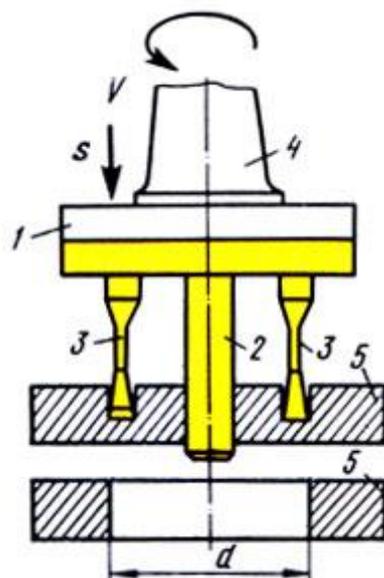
Вырезание отверстий в листовом металле: 1 - оправка, 2 - направляющий стержень, 3 - резцы, 4 - хвостовик, 5 - деталь
